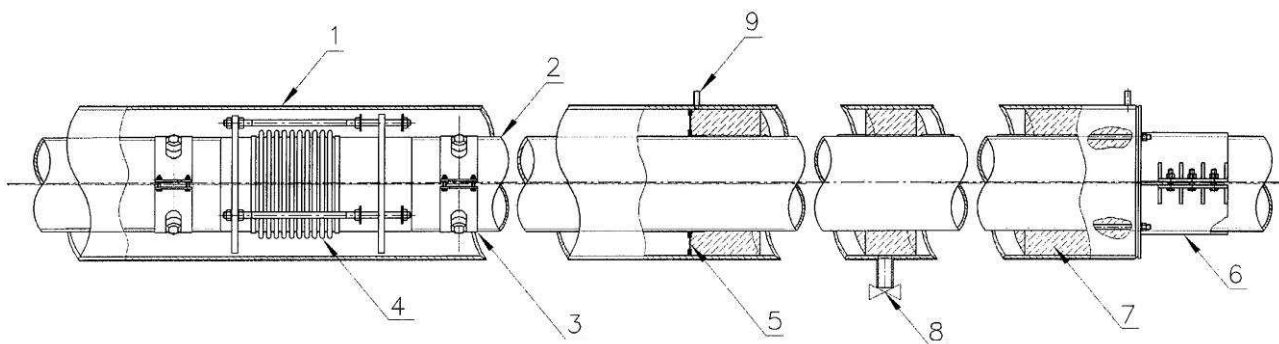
Общий вид герметичной проходки трубопровода: 1 – защитный кожух; 2 – рабочая труба; 3 – опорно-центрирующие кольца; 4 – сильфонный компенсатор; 5 и 6 – фланцы; 7 – межтрубные бетонные пробки; 8 – раструб; 9 – раструб для закачки ингибитора коррозии
